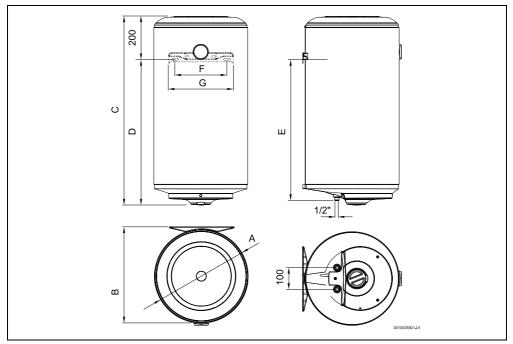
Dimensões em mm (montagem mural, instalação vertical)
